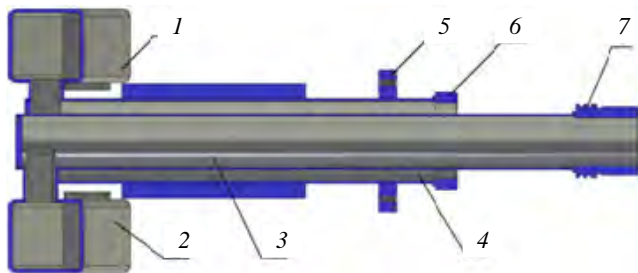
Общий вид водяного коллектора, основные элементы: 1 — напорный коллектор-ресивер; 2 — сливной коллектор-ресивер; 3 — сливной трубопровод; 4 — напорный трубопровод; 5 — фланец развязки вакуум—атмосфера; 6 — присоединительный фланец к напорной магистрали; 7 — присоединительный фланец к сливной магистрали
